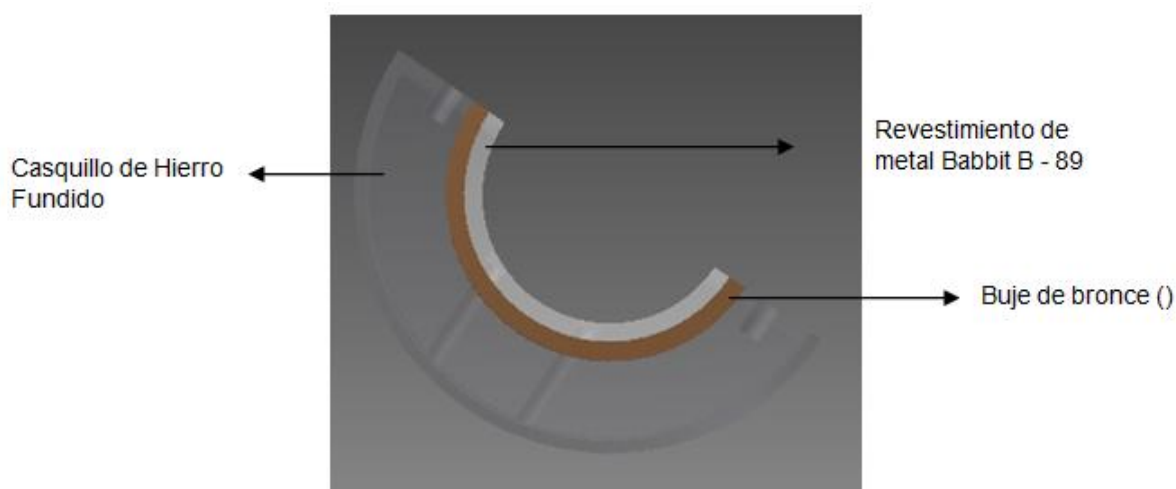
Materiales que componen el cojinete de deslizamiento.
